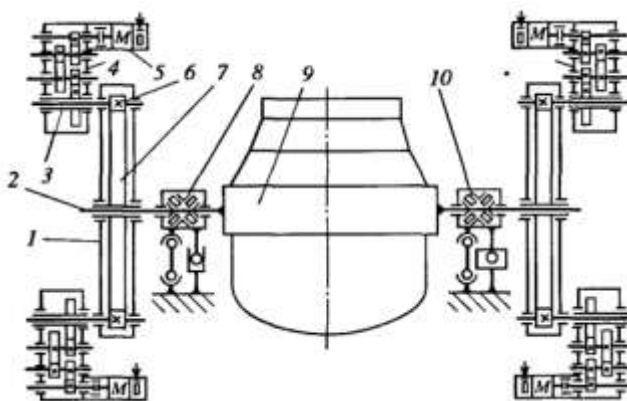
Кинематическая схема навесного многодвигательного привода конвертера
